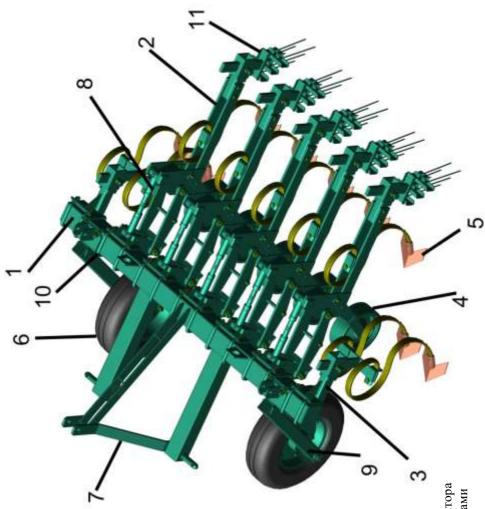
Общий вид культиватора КМЛ-1,4 с пружинными боронками
